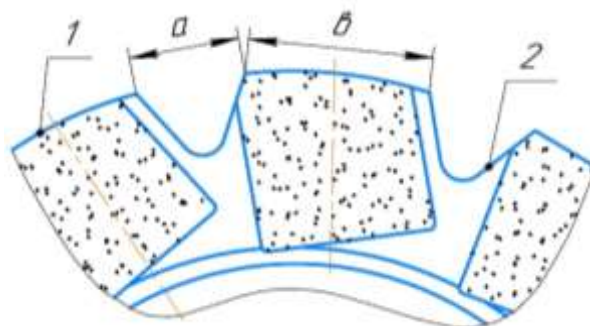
Часть периферийного диска с разделительными канавками и наплавкой обратного конуса шарошки.
